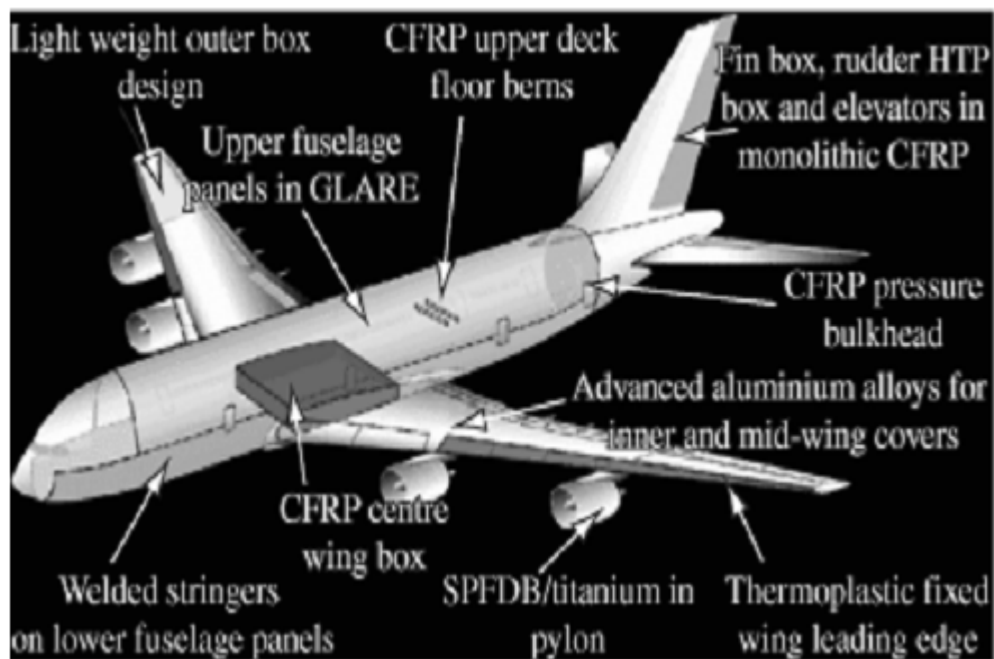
Componentes soldados em uma aeronave. Fonte: www.ewf.eb
